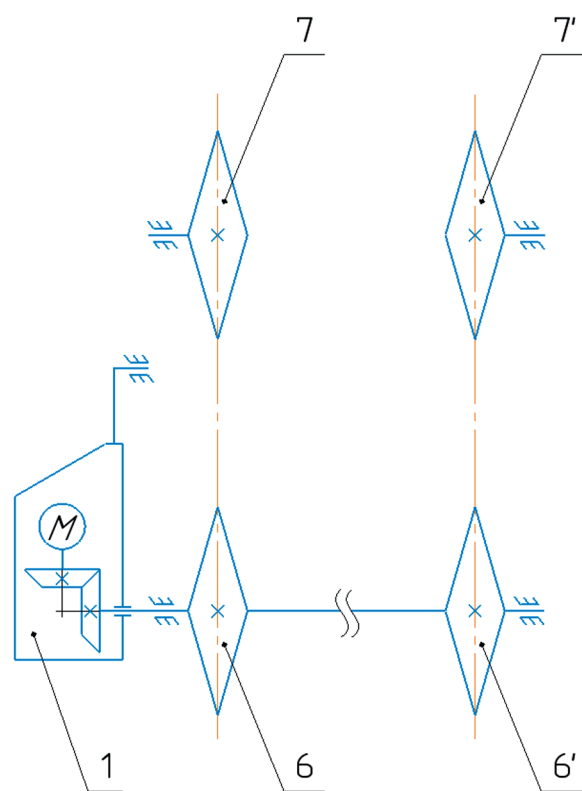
Предлагаемая кинематическая схема модернизации роторной парковки: 1 — мотор-редуктор; 6 и 6' — ведущая звездочка привода; 7 и 7' — направляющие звездочки привода
